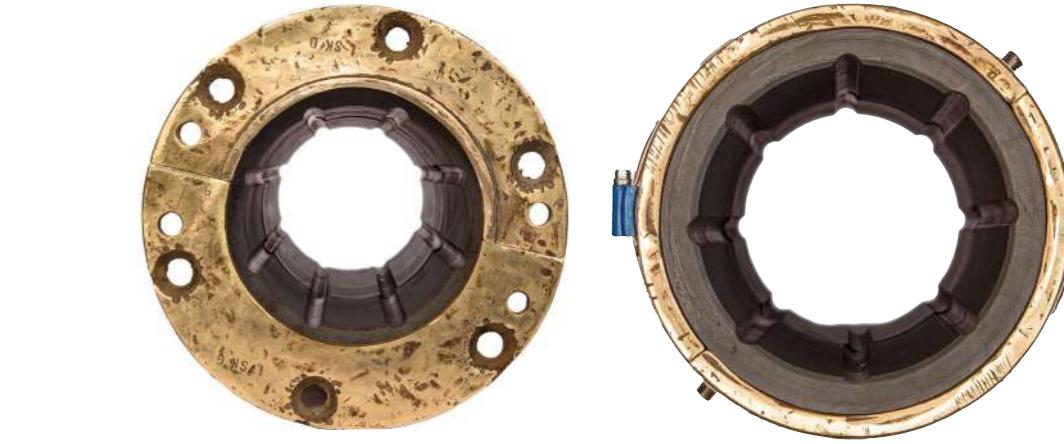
Nacrt sklopa ležaja i čahure/ Drawing of the bearing and sleeve assembly
